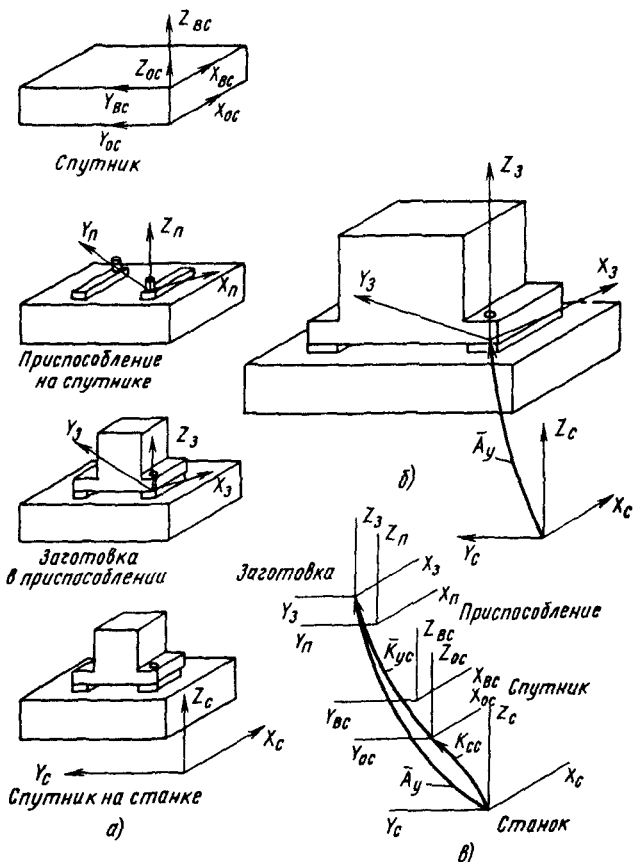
Схемы формирования положения заготовки на спутнике и на станке: а — схема этапов установки, б — схема образования вектора-размера установки в системе координат станка, в — векторная схема
